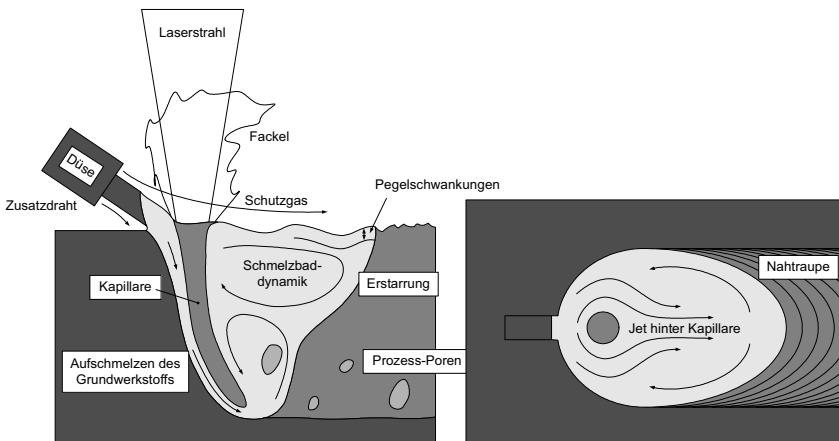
Laserschweißprozess mit einigen Teilvorgängen
